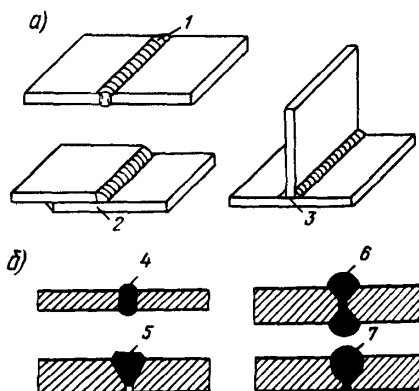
Сварные соединения и швы: а — сварные соединения; б — сварные швы; 1 — встык; 2 — внахлестку; 3 — тавровое; 4 — без скос; 5 — V-образный; 6 — X-образный; 7 — U-образный
